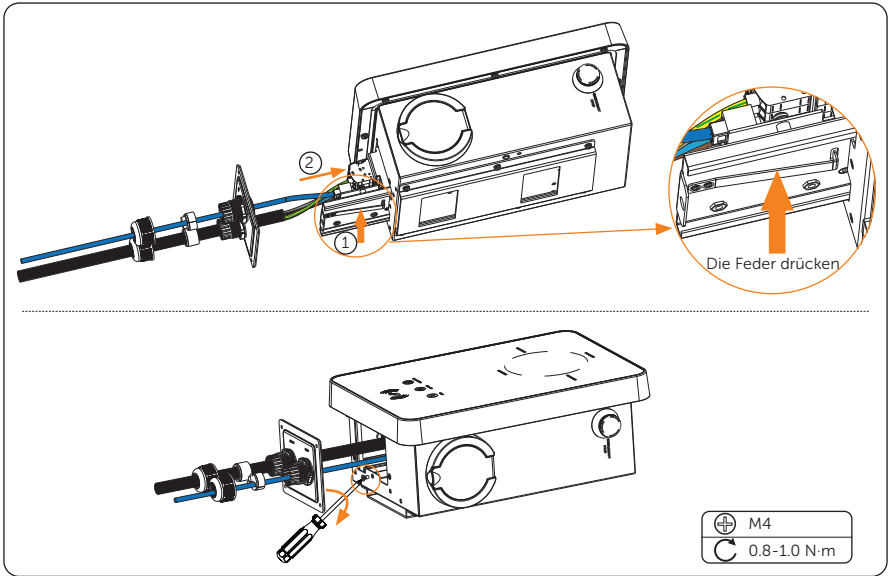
Die Grundplatte der Kommunikationsplatine anschrauben
